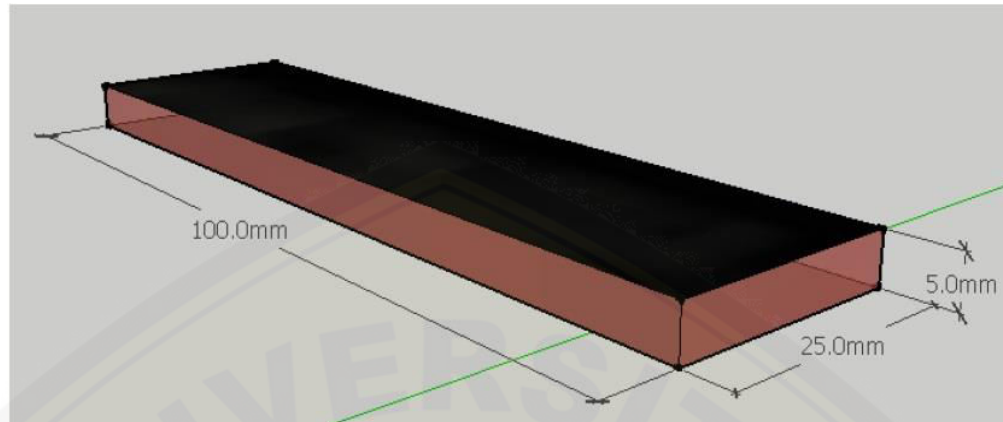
Dimensi spesimen (Standar ASTM D3039, 2000)
